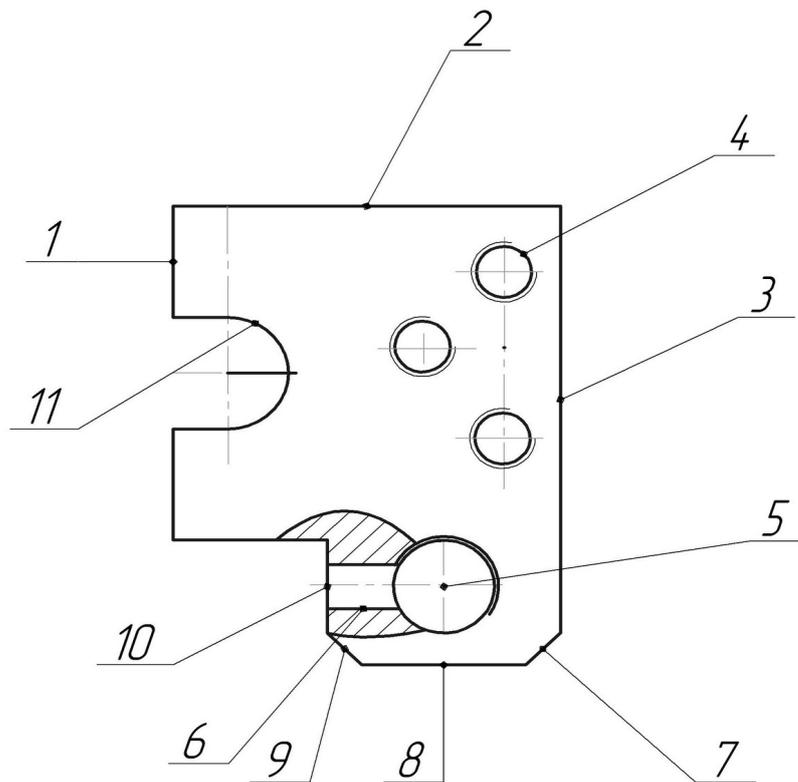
Нумерация поверхностей детали рейка зубчатая
